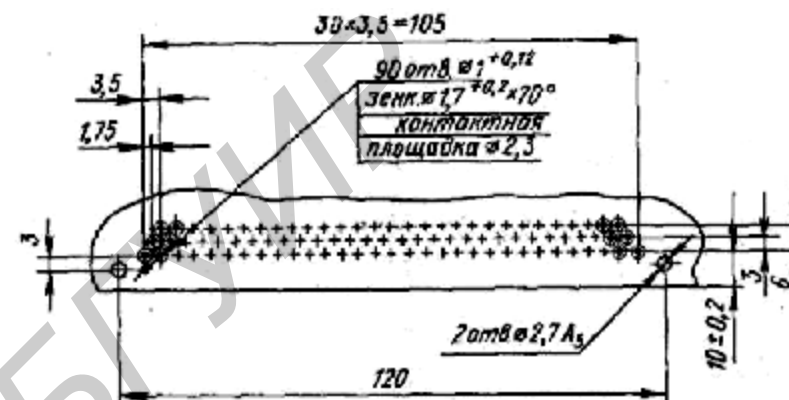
Разметка посадочного места для вилки разъёма ГРПМ1-90ШУ на печатной плате
